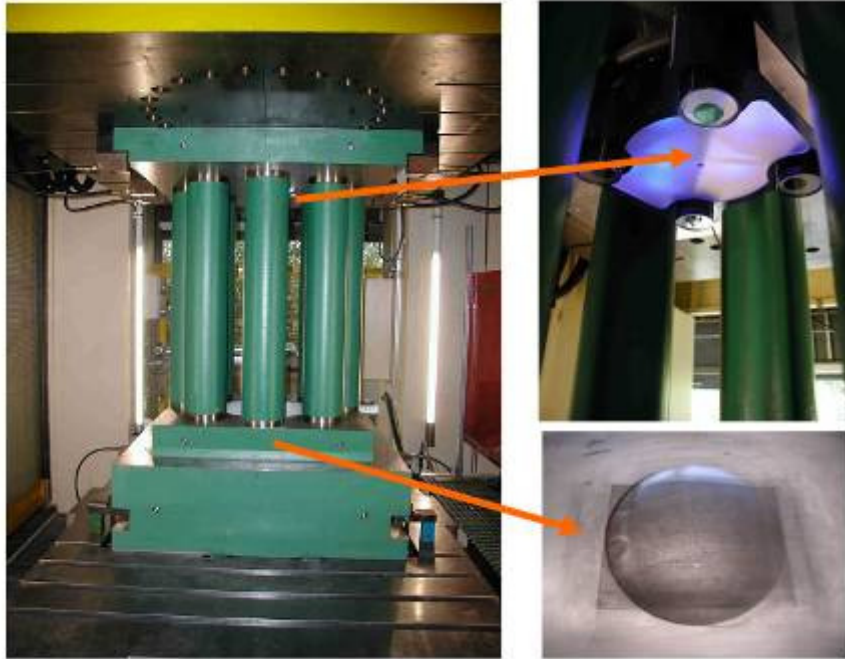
MBT-Werkzeug im eingebauten Zustand und umgeformte MBT-Probe bis zum Anriss (AZ31, $s = 1.24 \text{ mm}$)
